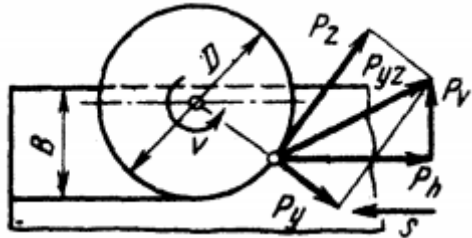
Схема сил при несиметричному зустрічному фрезеруванні
